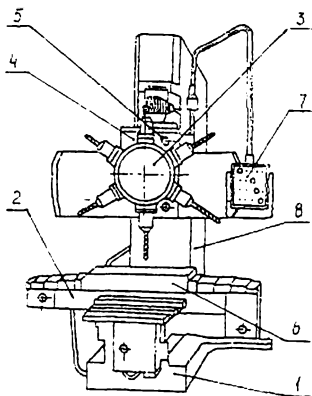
Вертикально-свердильний верстат 2P135Ф2-1
